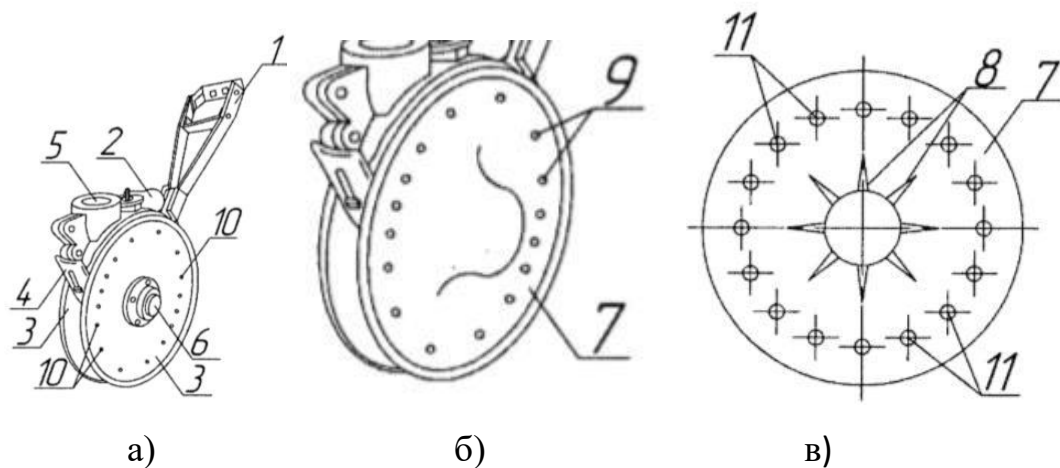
Схема модернізованого дводискового сошника: а) загальний вигляд сошника; б) вид бічної накладки диска; в) точки механічного кріплення накладки
